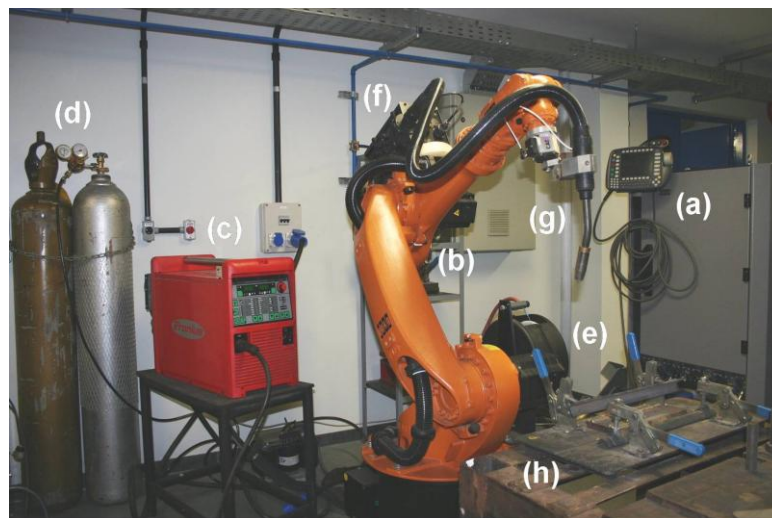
Célula robótica de soldagem do LRSS. (a) Painel de controle do robô manipulador; (b) Robô manipulador da Soldagem; (c) fonte de soldagem; (d) cilindro de gás; (e) rolo de arame; (f) alimentador de arame; (g) tocha de soldagem e (h) mesa de soldagem com grampos de fixação.
